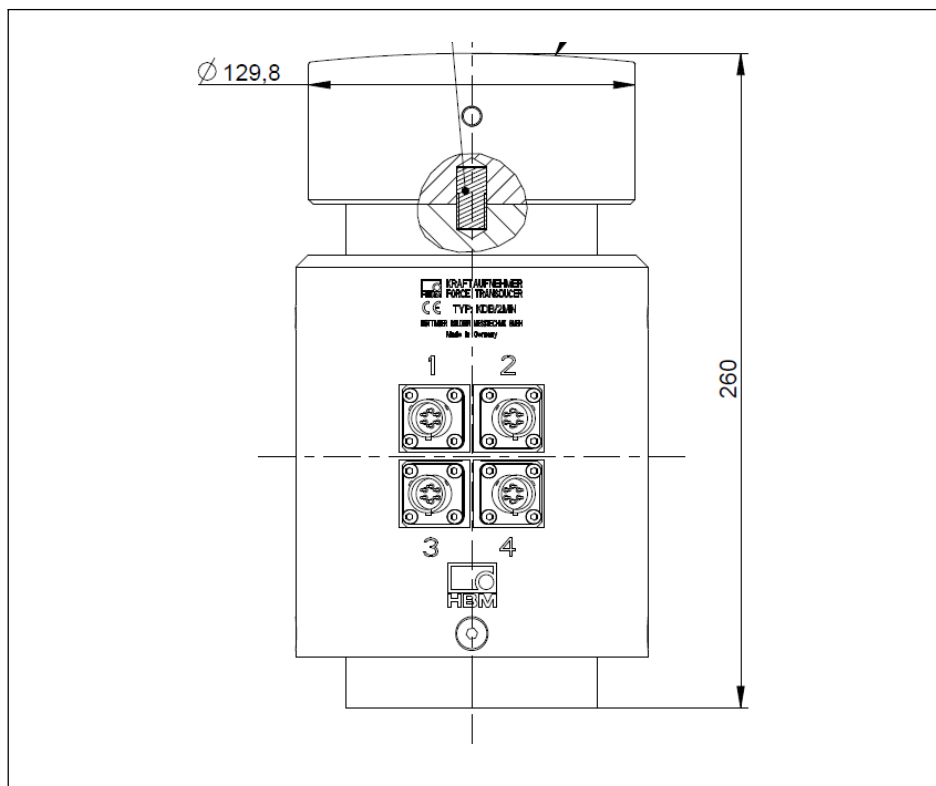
Dimensioni per l'uso con bottone d'introduzione del carico convesso
